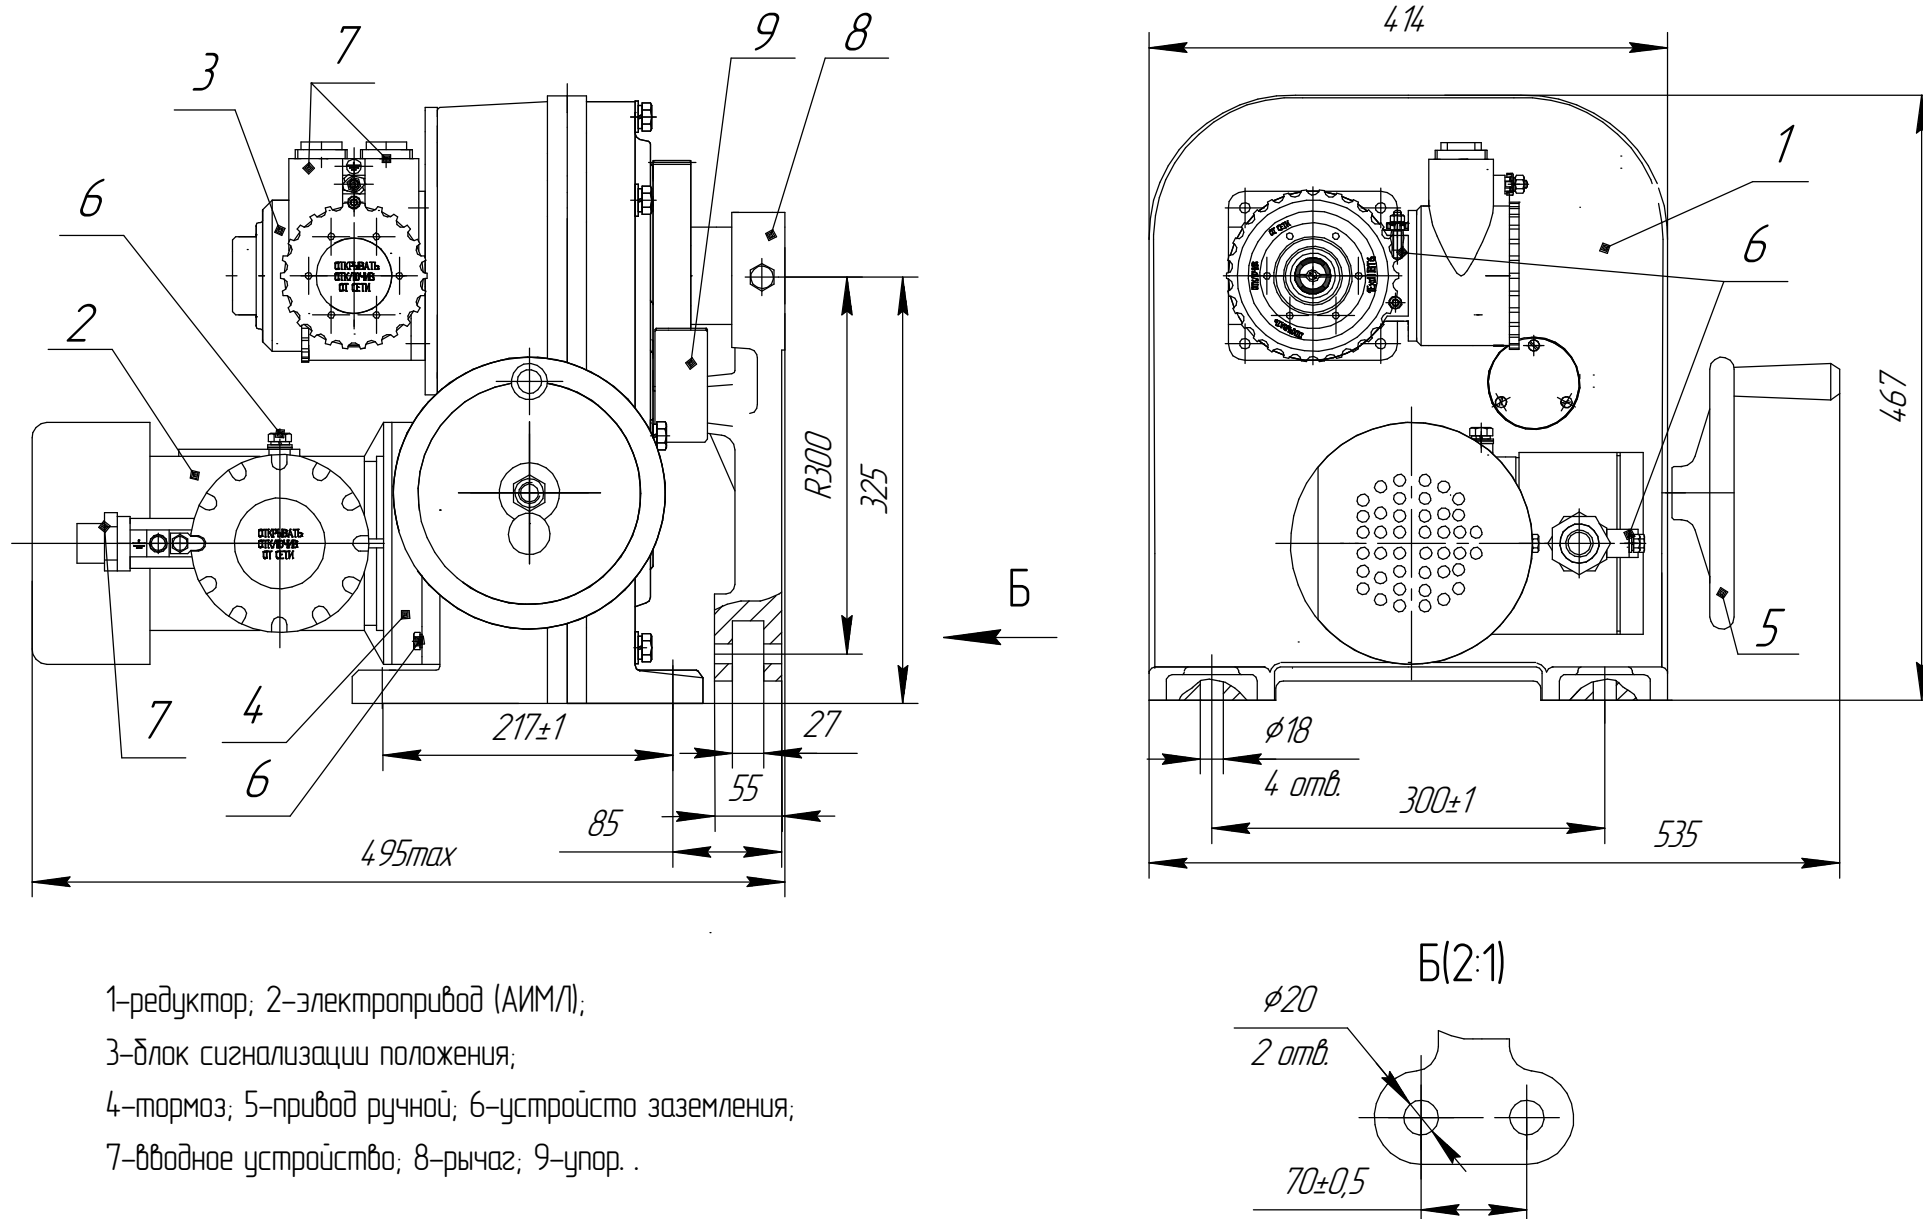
Общий вид, габаритные и присоединительные размеры механизма МЭО-II BT4 группы 1600
